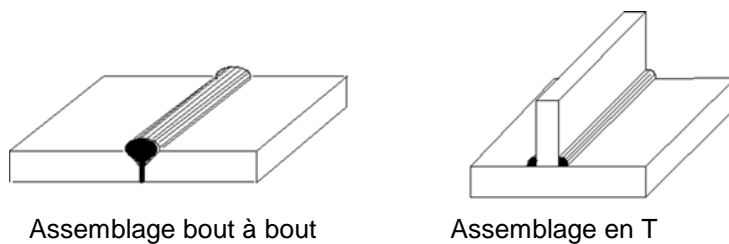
Exemple d'assemblage de deux pièces par soudure
